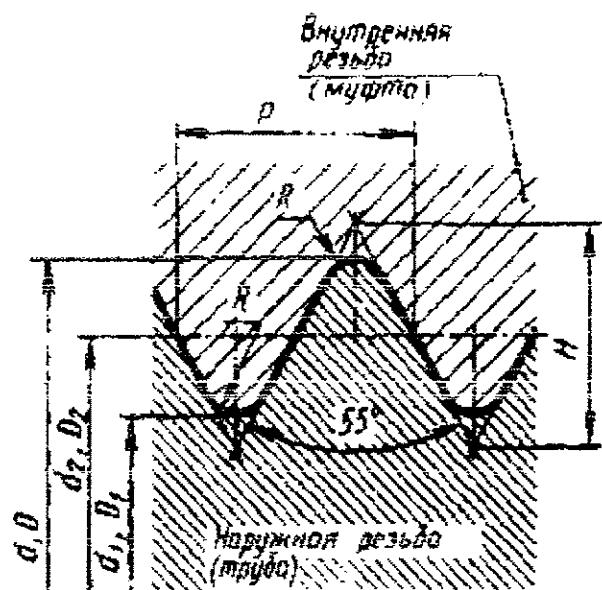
Профиль и основные размеры трубной цилиндрической резьбы
